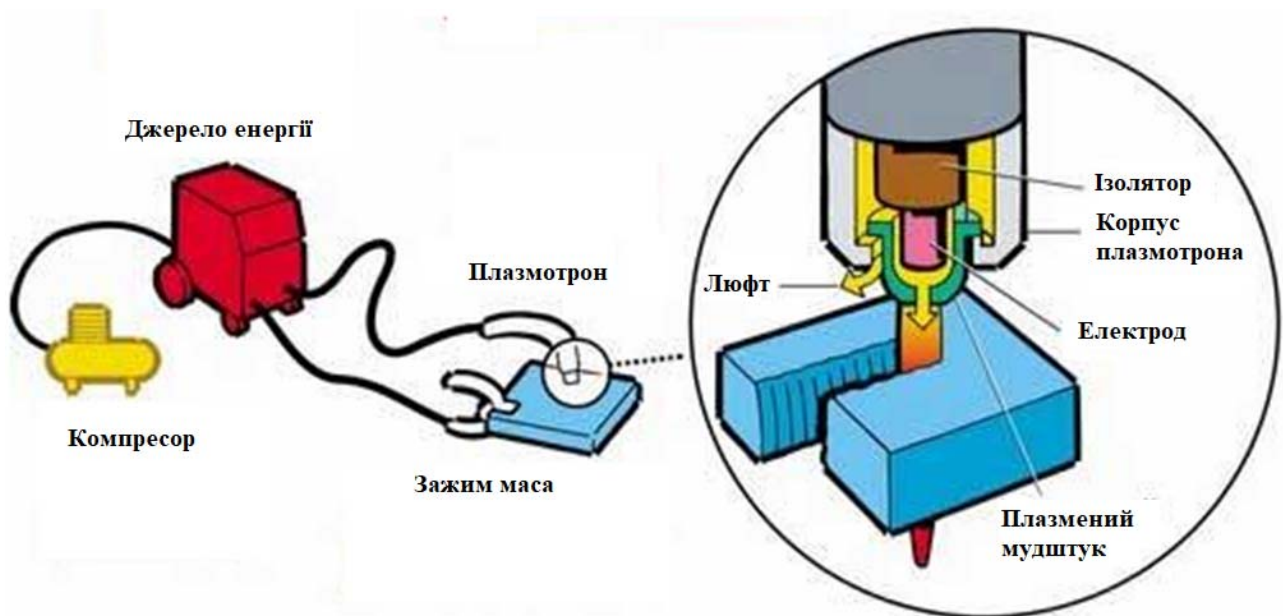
Спрощена схема плазмової обробки металів
